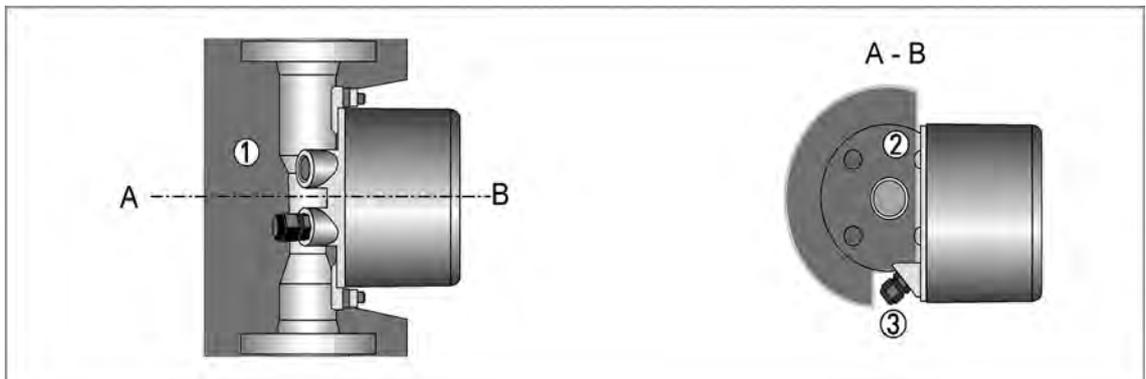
Тепловая изоляция - поперечное сечение
